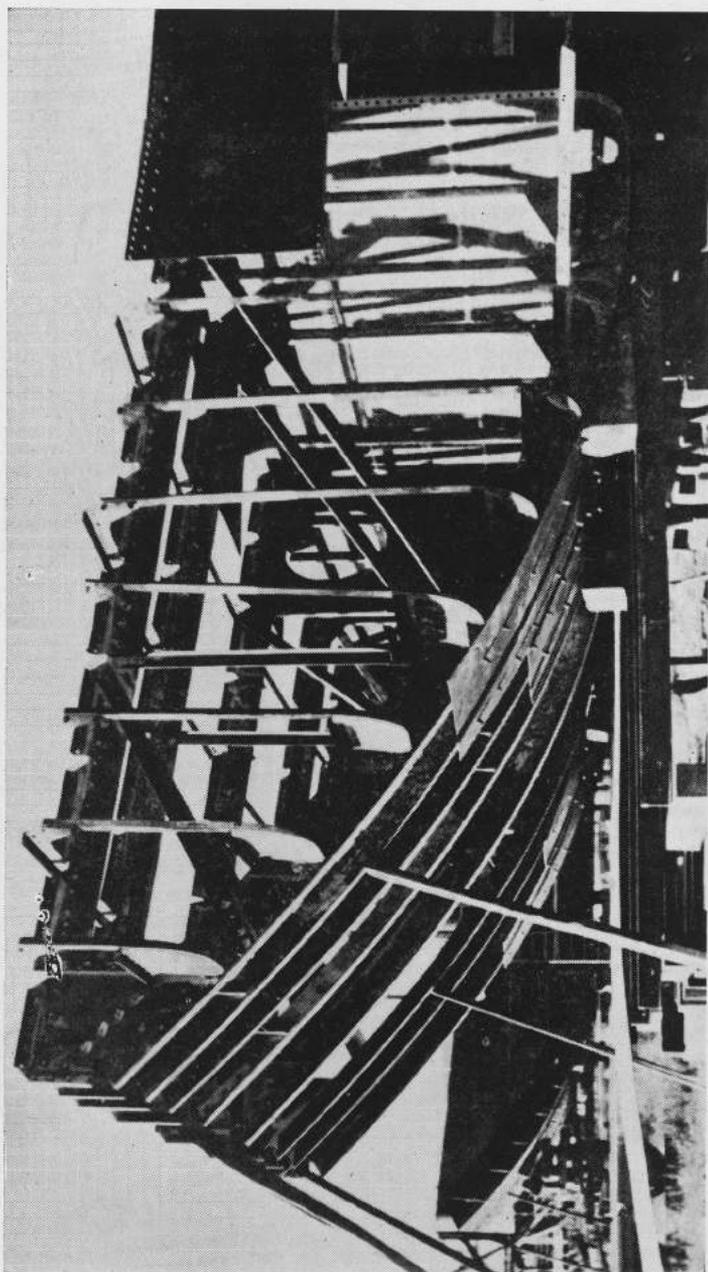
Détail de l'avant d'une barge de 600 T.
